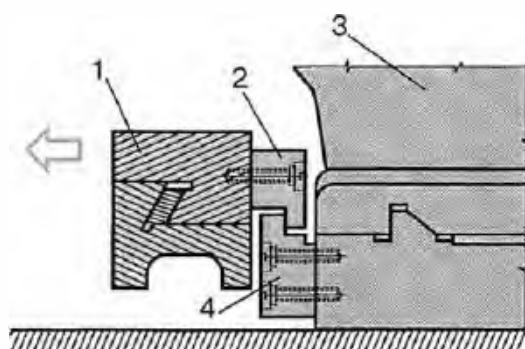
ПРИВ'ЯЗКА СУПОРТА ДО ЗАДНЬОЇ БАБКИ:
